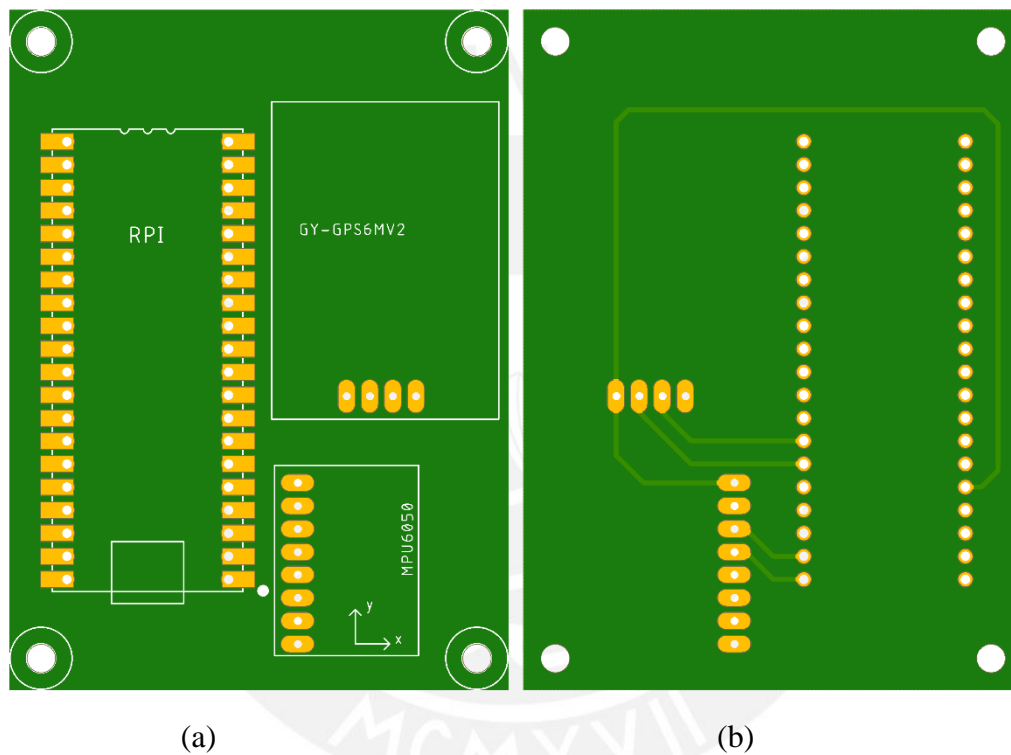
(a) Vista delantera del PCB. (b) Vista trasera del PCB.
